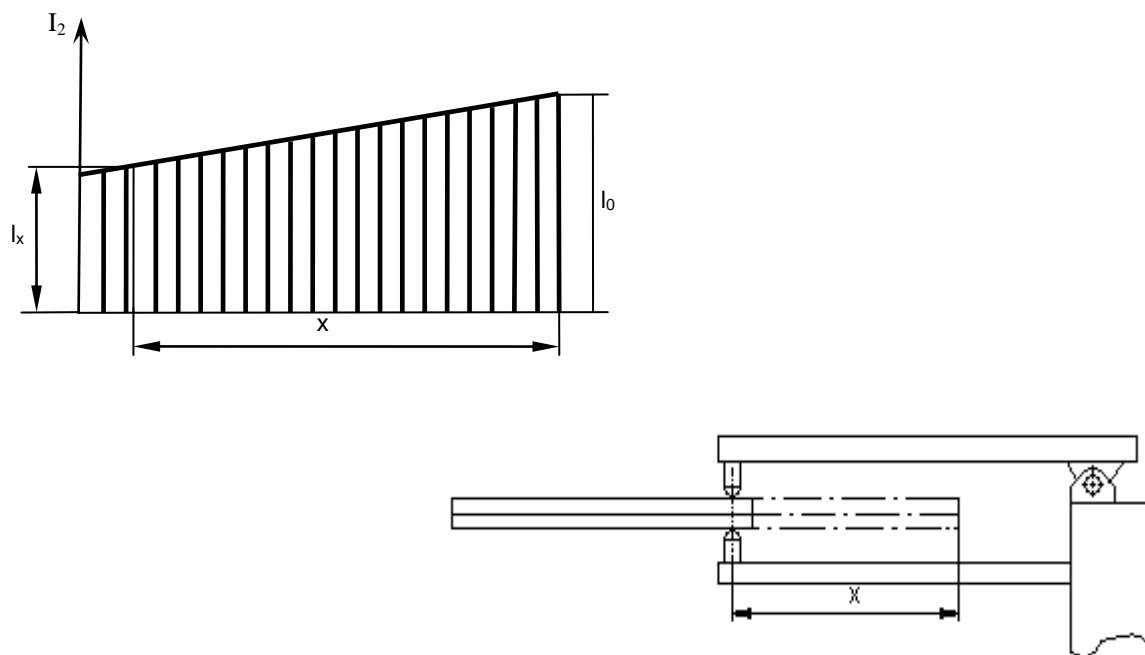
Изменение тока в сварочной цепи при введении в контур машины магнитного металла
